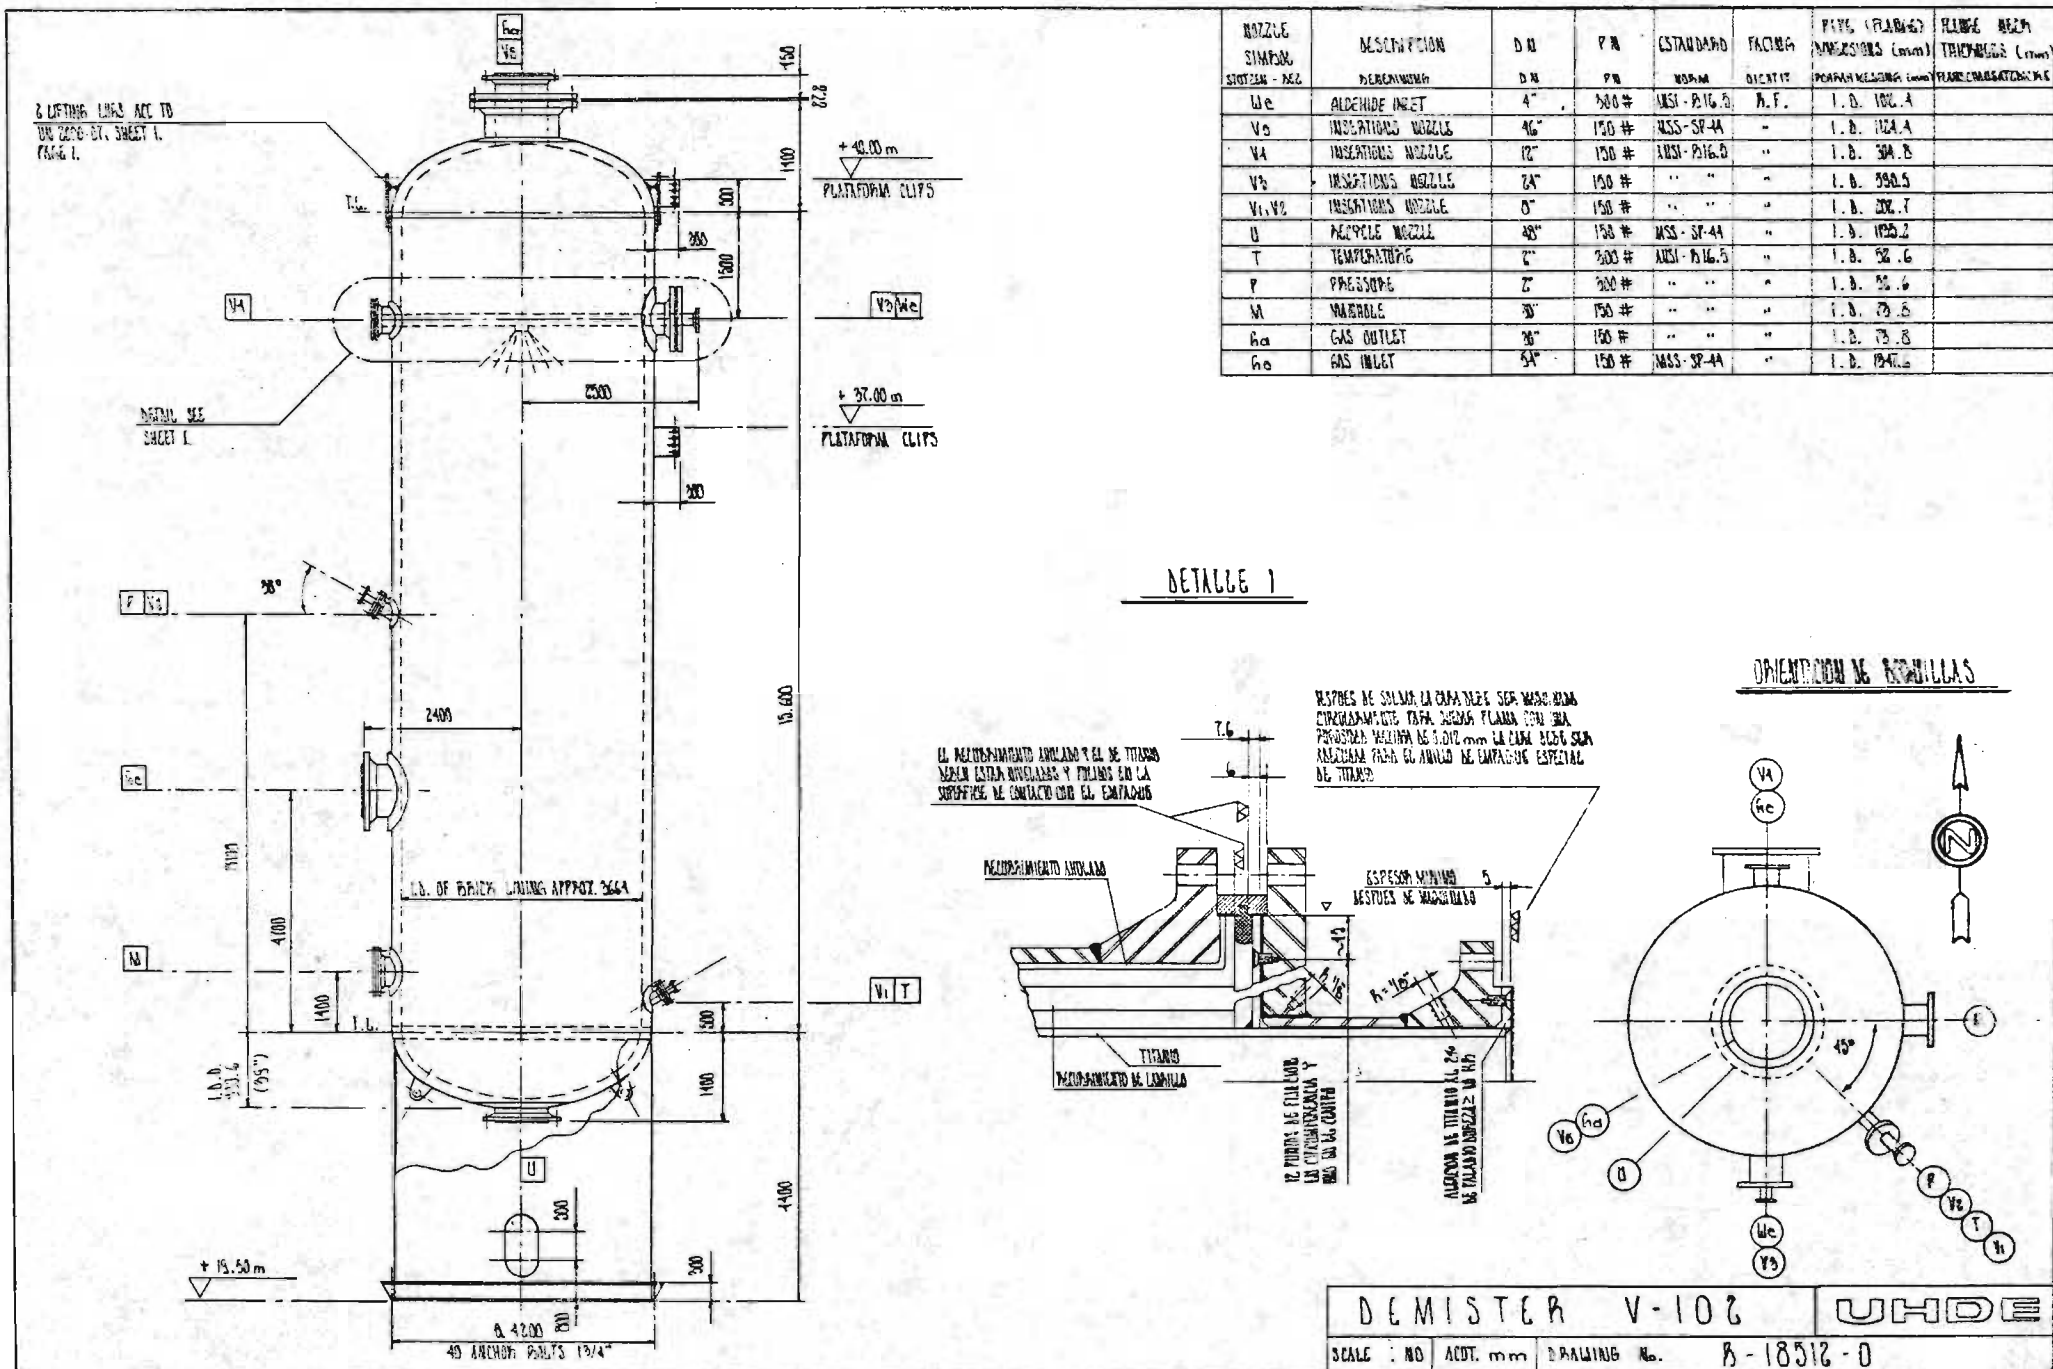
Dibujo Mecanico del Equipo V-102.
